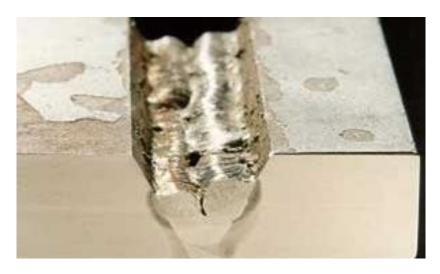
Fusión Incompleta entre Cordones de Soldadura
